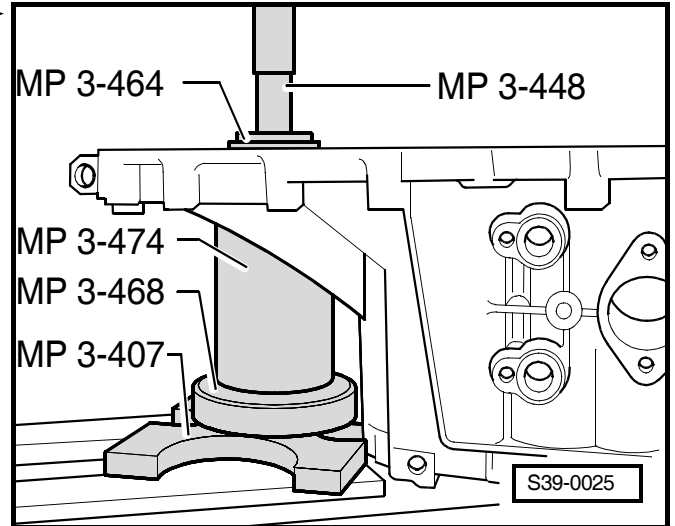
Déposer et poser la douille de serrage pour l'axe du pignon conique du différentiel
